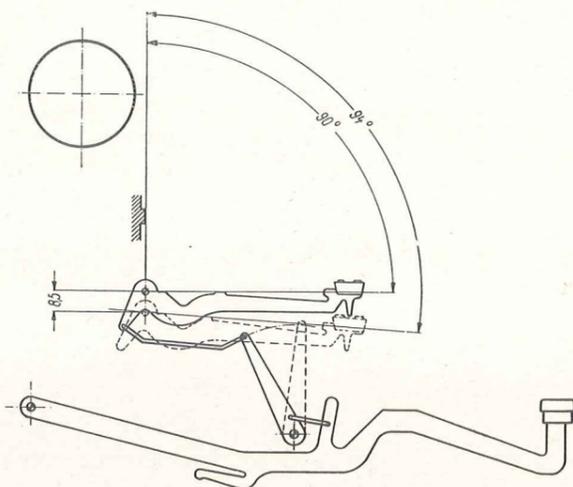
Sechsgliedriger Typenhebelantrieb, bei dem sich die Zwischenhebel in die Typenhebel hineinbewegen
